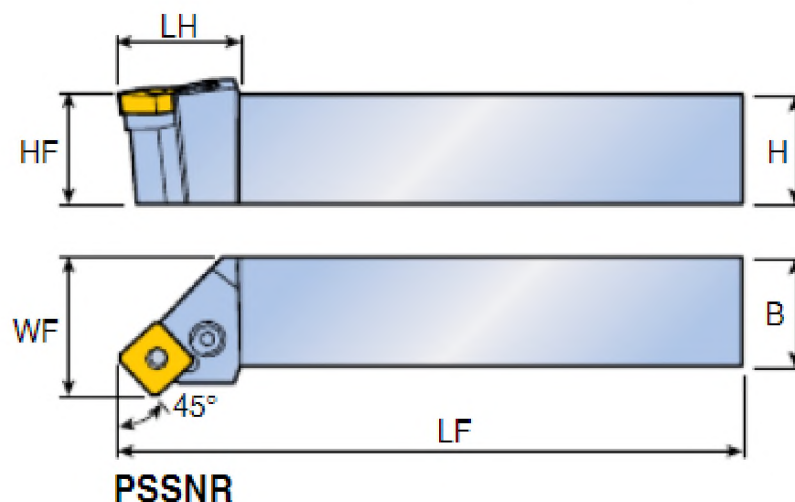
Державка PSSNR/L 2525M12 [1, с. A76]:
